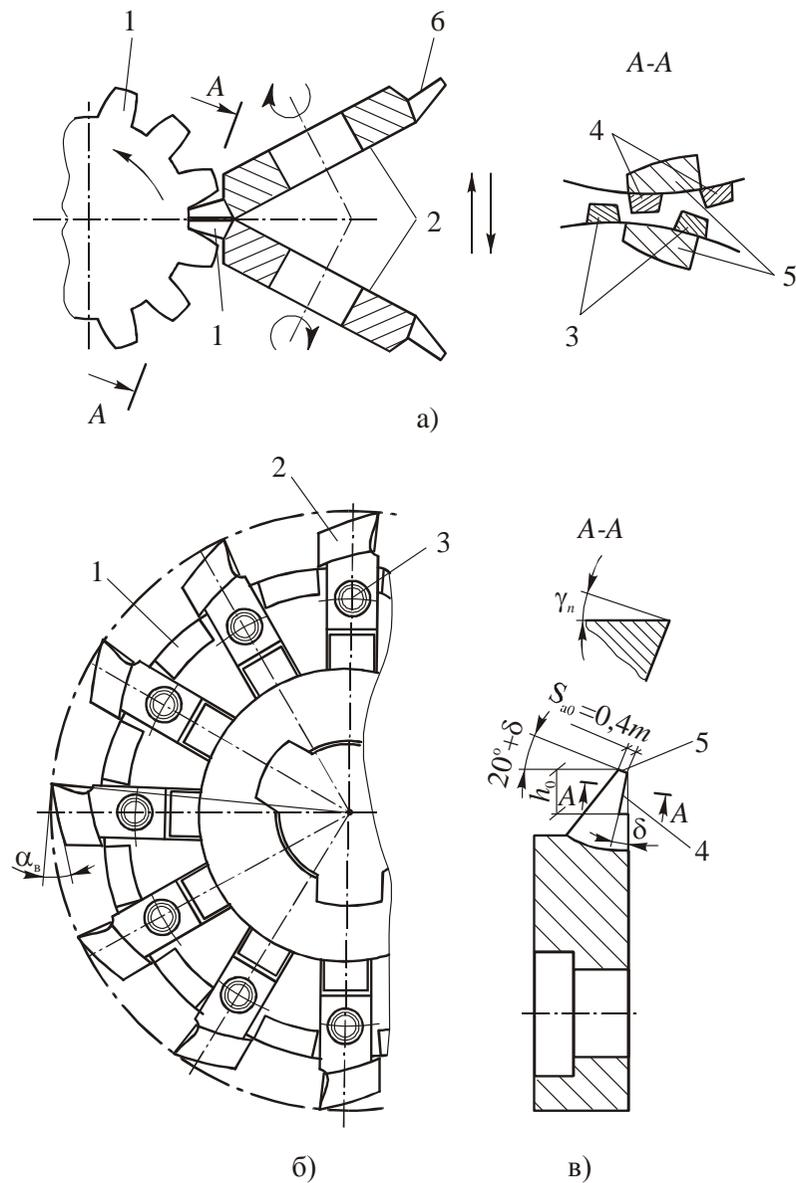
Дисковая зуборезная фреза: а – схема чистовой обработки зубьев конического колеса; б – конструкция сборной фрезы; в – нож фрезы
